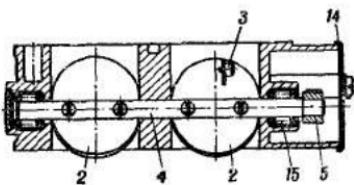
Ограничитель максимального числа оборотов коленчатого вала двигателя:
